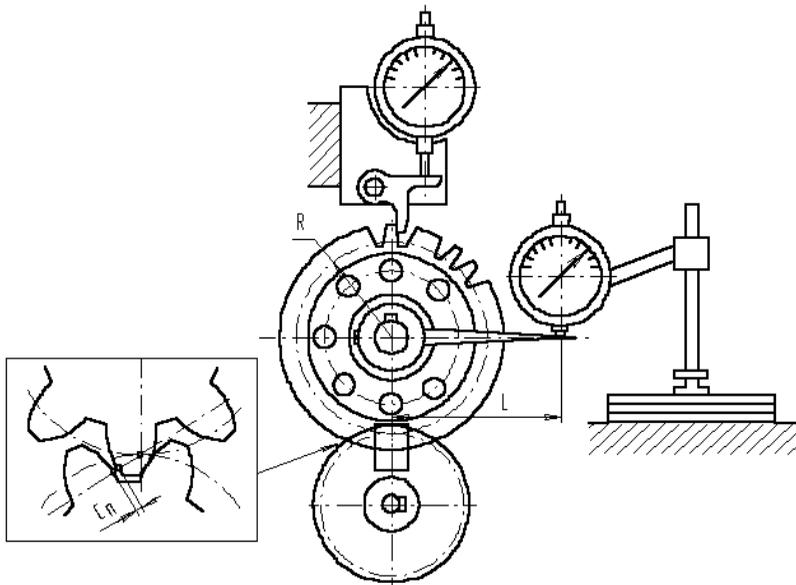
Схема контроля зазора в зацеплении зубчатых колес индикаторами
